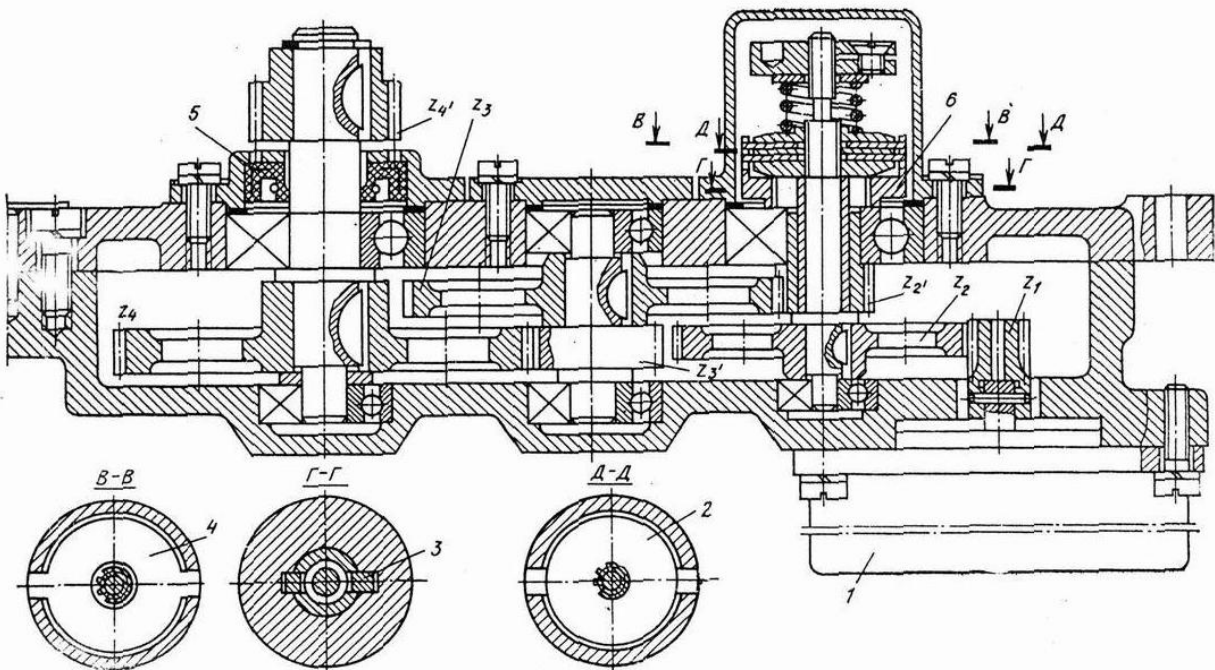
Редуктор приводу обертання антени РЛС
